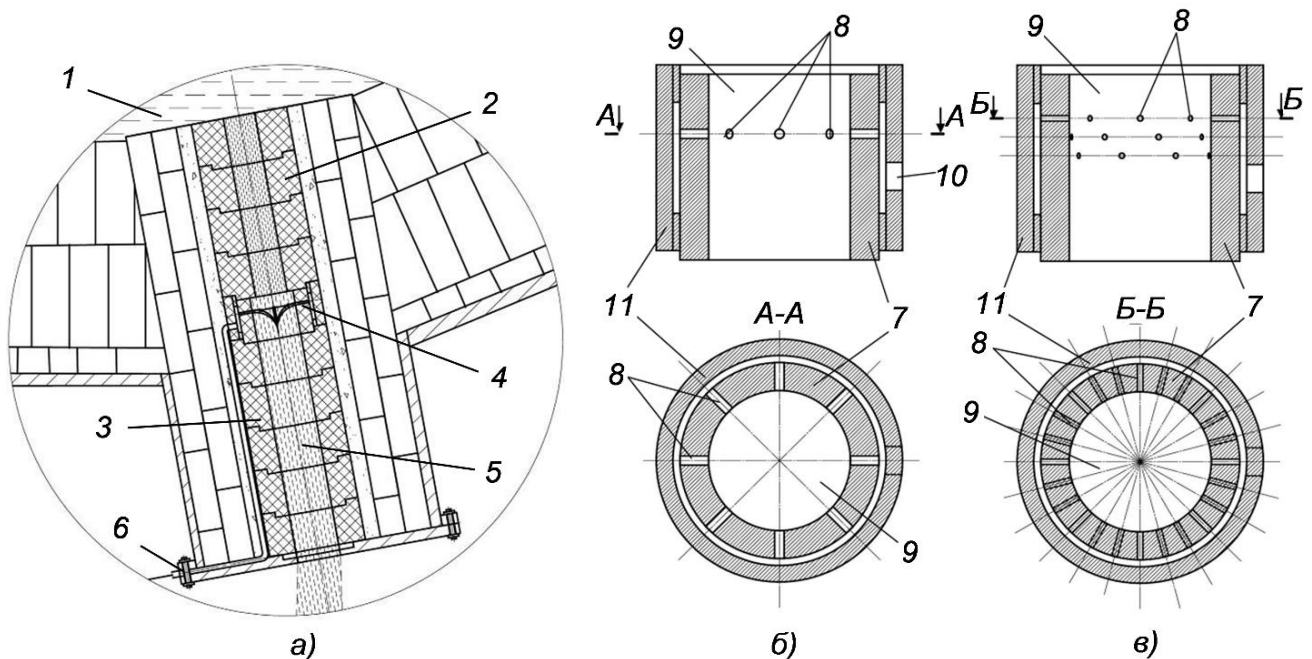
Схема двокамерного сталевипускного каналу з продувним блоком (а) і варіанти виконання блоків сталевипускного каналу для обробки розплаву газом (б, в): 1 – металевий розплав; 2, 3 – перша і друга камера сталевипускного каналу відповідно; 4 – блок з продувними вузлами (соплами); 5 – ГМП; 6 – насадка з газопідвідною лінією; 7 – продувний блок на 8 (а) і 24 (б) сопла; 8 – циліндричні сопла діаметром 10 мм (а) і 5 мм (б); 9 – робочий простір; 10 – отвір для підведення газу; 11 – зовнішня частина блоку.
